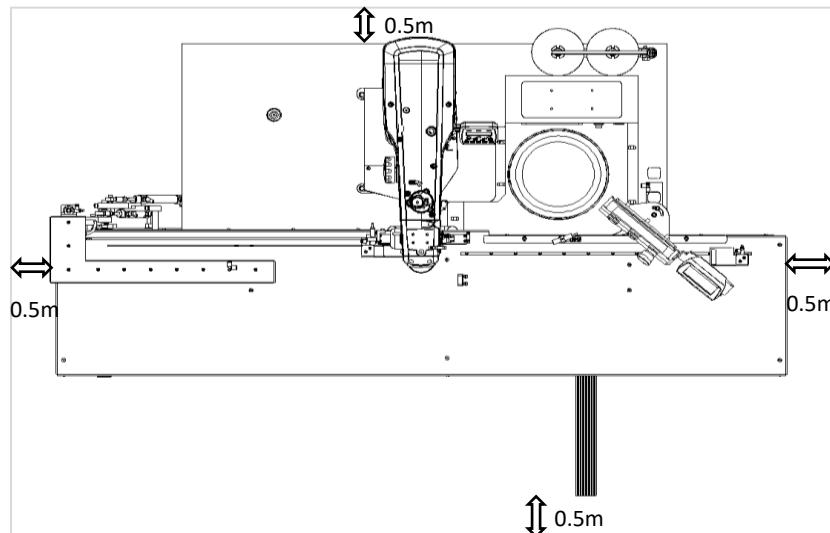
摆放设备周围空间要求 Figure 4.1 Space required around machine
